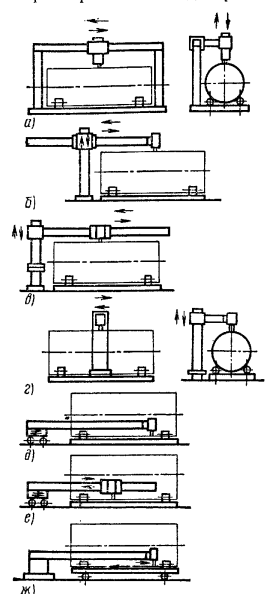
Типовые схемы компоновок установок для электродуговой сварки прямолинейных стыковых швов цилиндрических изделий без прижима свариваемых кромок
